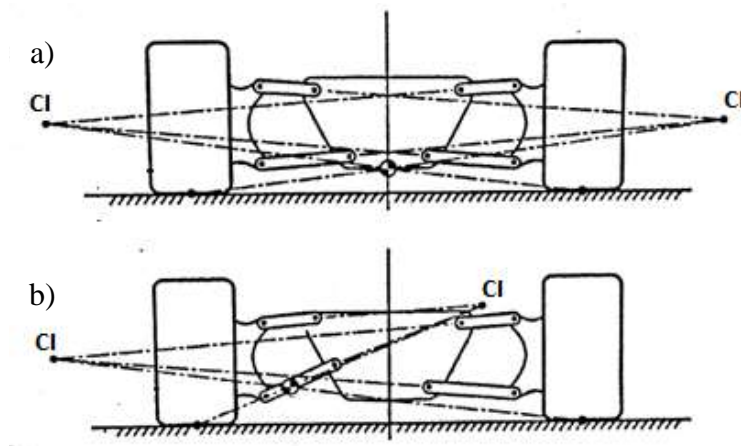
Geometría de vista frontal. (Milliken & Milliken)
